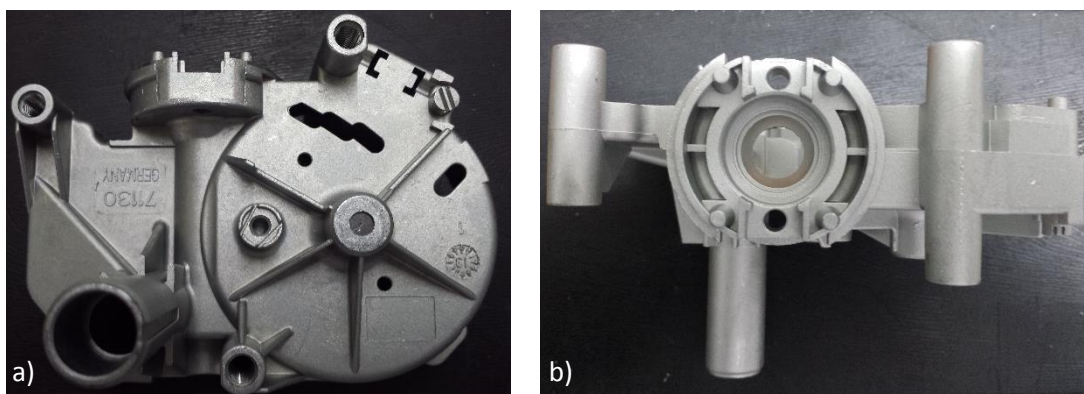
Vista frontal (a) e de topo (b) da *metallic gear housing* nº 324
